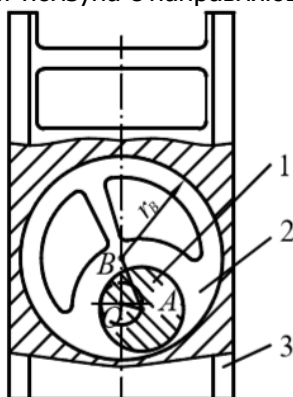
Схема кривошипно-кругового механизма: 1 – кривошип; 2 – промежуточное звено; 3 – ползун
